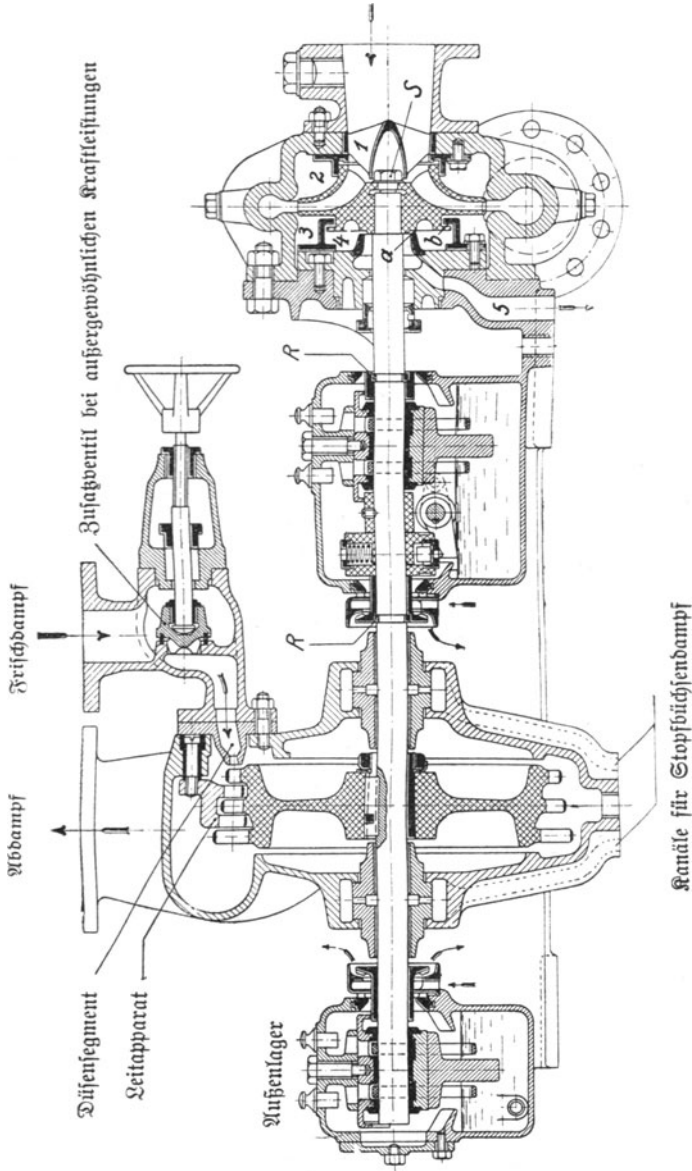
Längsschnitt durch die Turbinenpumpen. Die Wellenlager gegenüber den Stopfbüchsen der Turbinen haben Ventilationsringe R, um zu verhindern, daß der aus Stopfbüchsen austretende Dampf in die Kammer der Lager gelangen kann. 4 = Entlastungskammer zur Aufhebung der axialen Verschiebung der Welle nach der Turbine zu.
